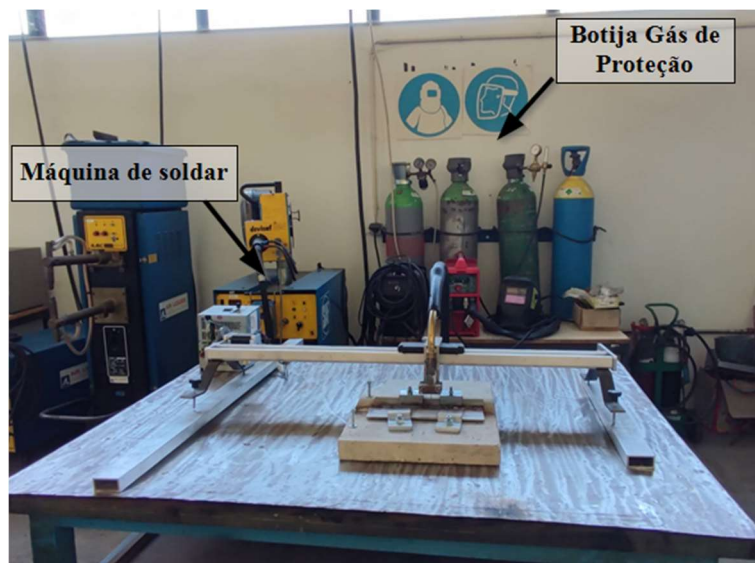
Área de trabalho utilizada nas soldaduras.
